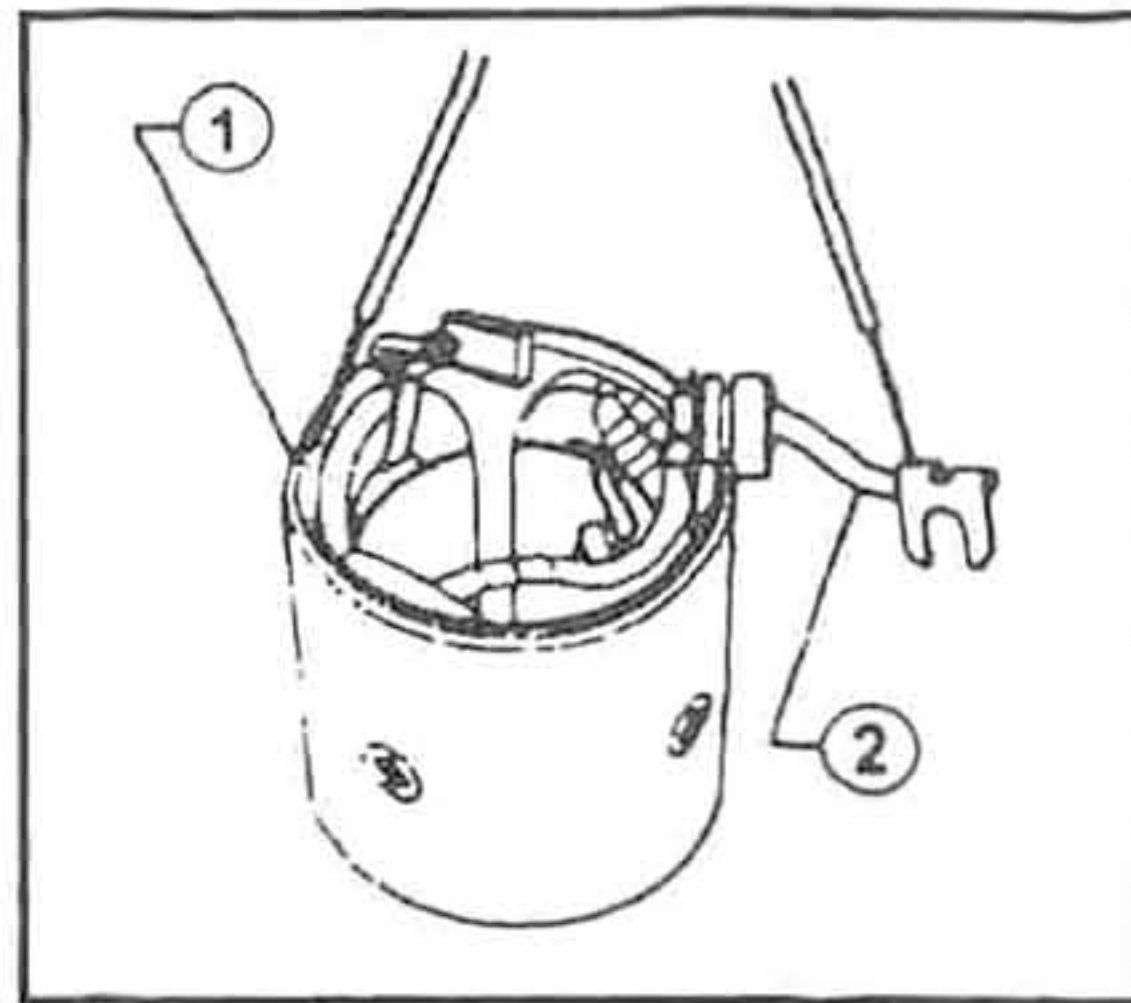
1. Корпус. 2. Плюсовой вывод обмотки возбуждения.
